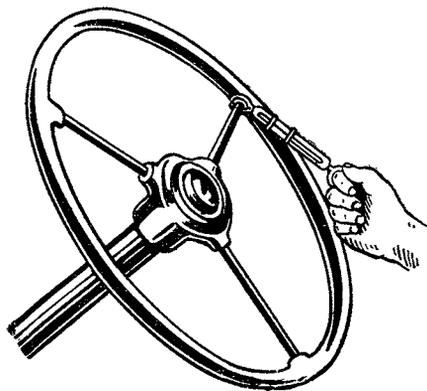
Проверка динамометром усилия поворота рулевого колеса
